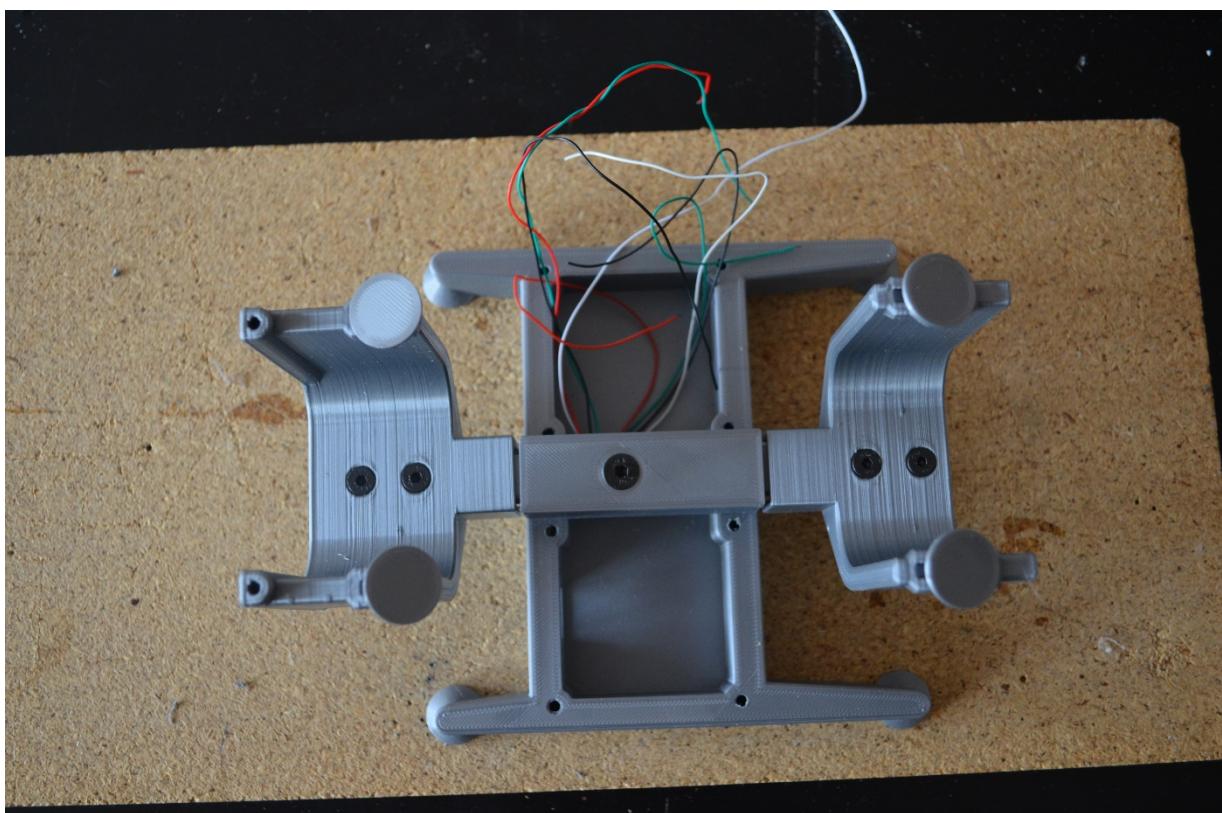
Etape 3 – supports avant & arrière de planeur installés.
